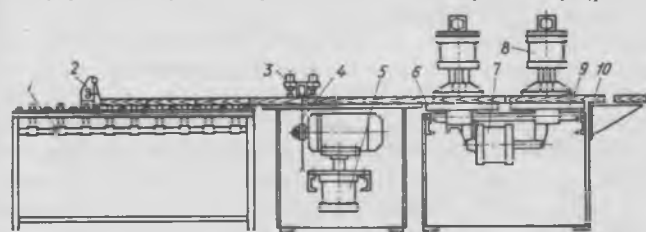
Агрегатный станок для стыковки короткомерных отрезков досок:
